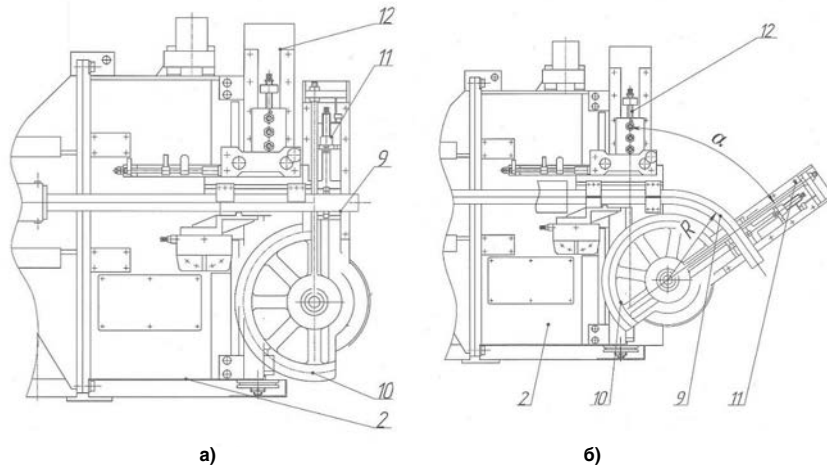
Схема гибки поворотным рычагом: а) исходное положение, вид сверху б) конечное положение гибки поворотным рычагом при повороте кронштейна на угол  $\alpha$ , вид сверху
